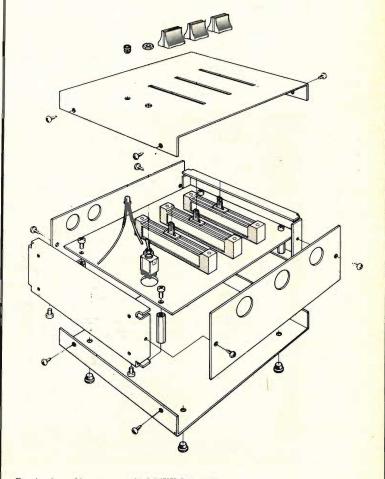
Assemblaggio generale dell'UK 716 dell'Amtron.
